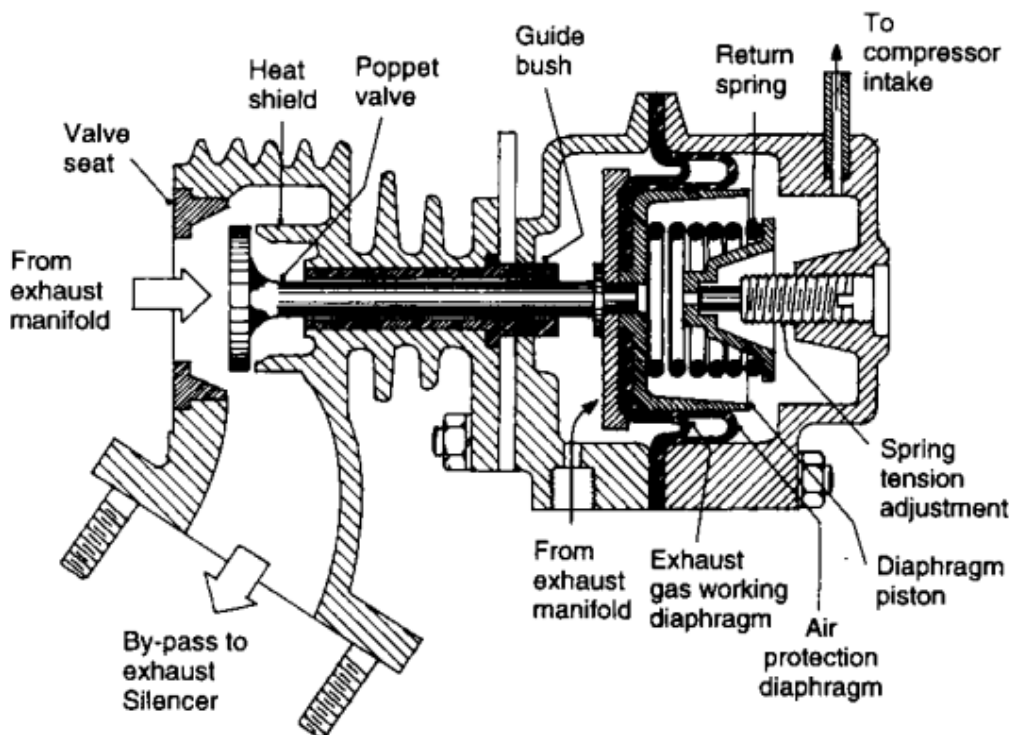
Pretlakový pneumatický aktuátor [16]
